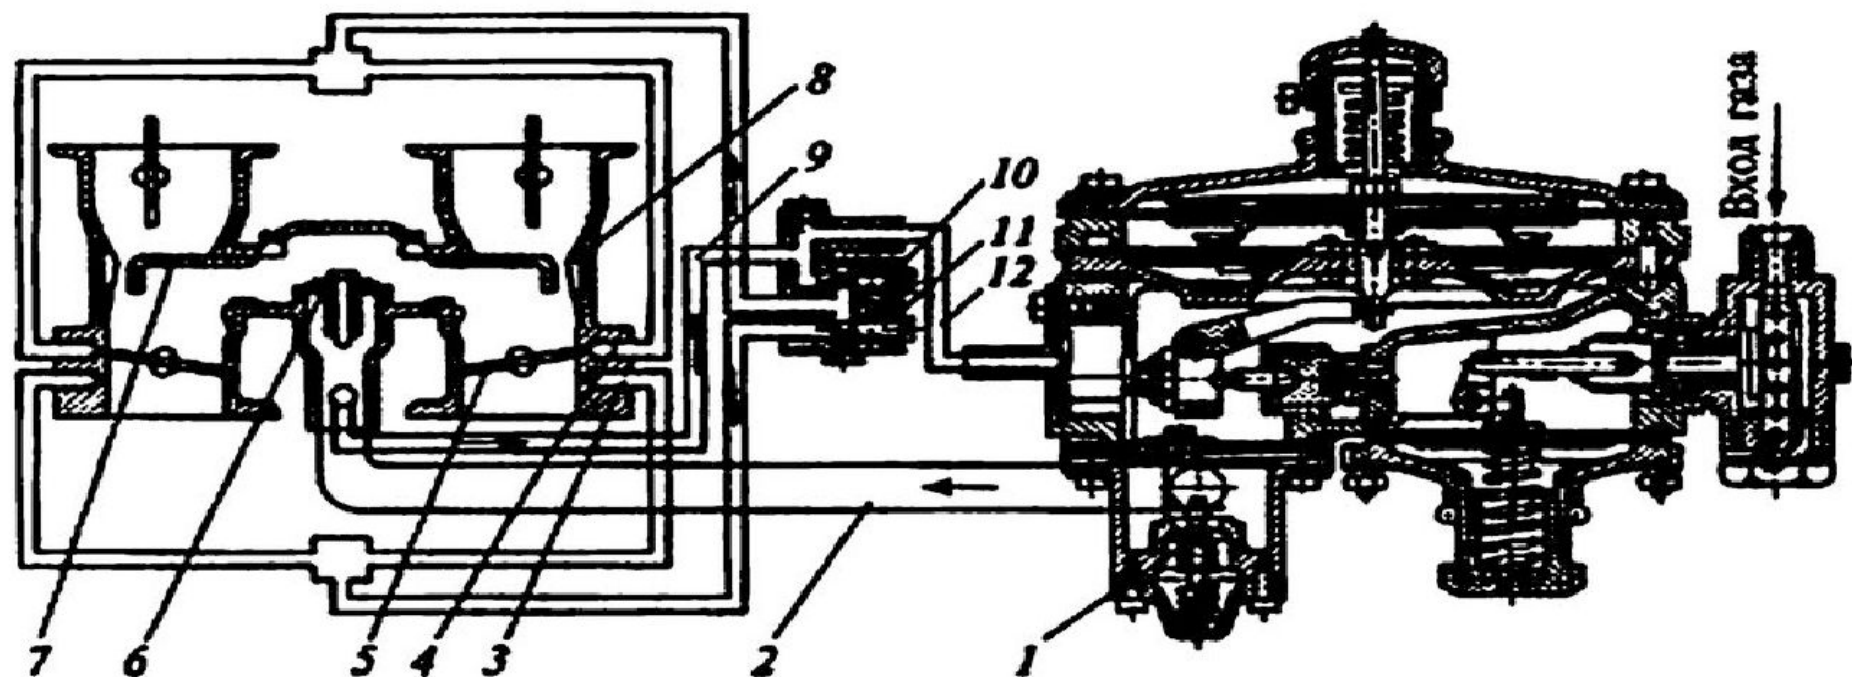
Схема соединения газового смесителя и двухступенчатого редуктора:
